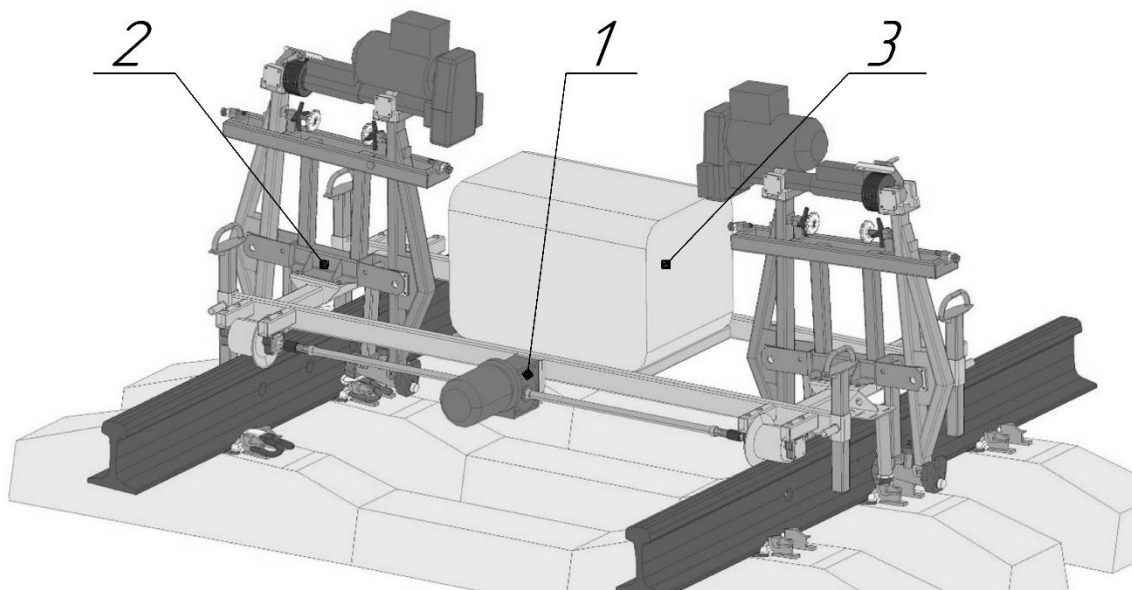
Установка для работы с рельсовым креплением Пандрол
